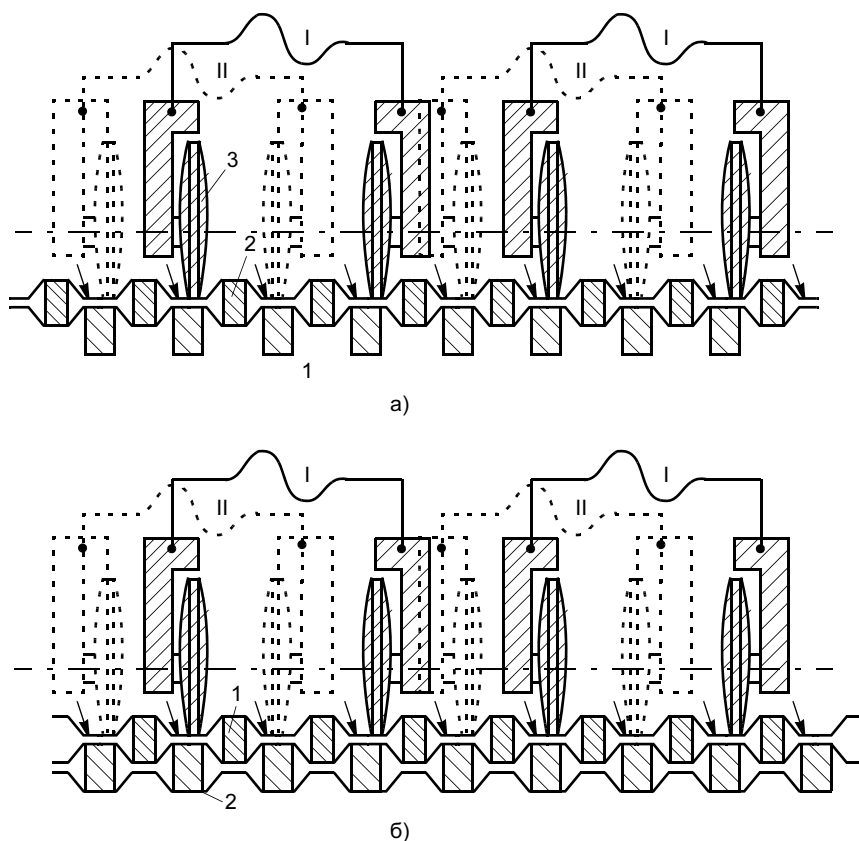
Схема сварки сотовой панели: а, б — первая и вторая позиции сварочного ролика соответственно
